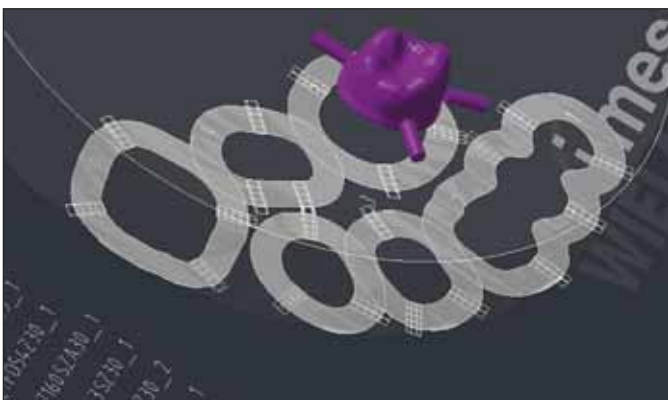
Im CAM-Modul werden die einzelnen Arbeiten auf die Rohlinge verteilt und die Fräsbahnen für die Fräsmaschine berechnet
